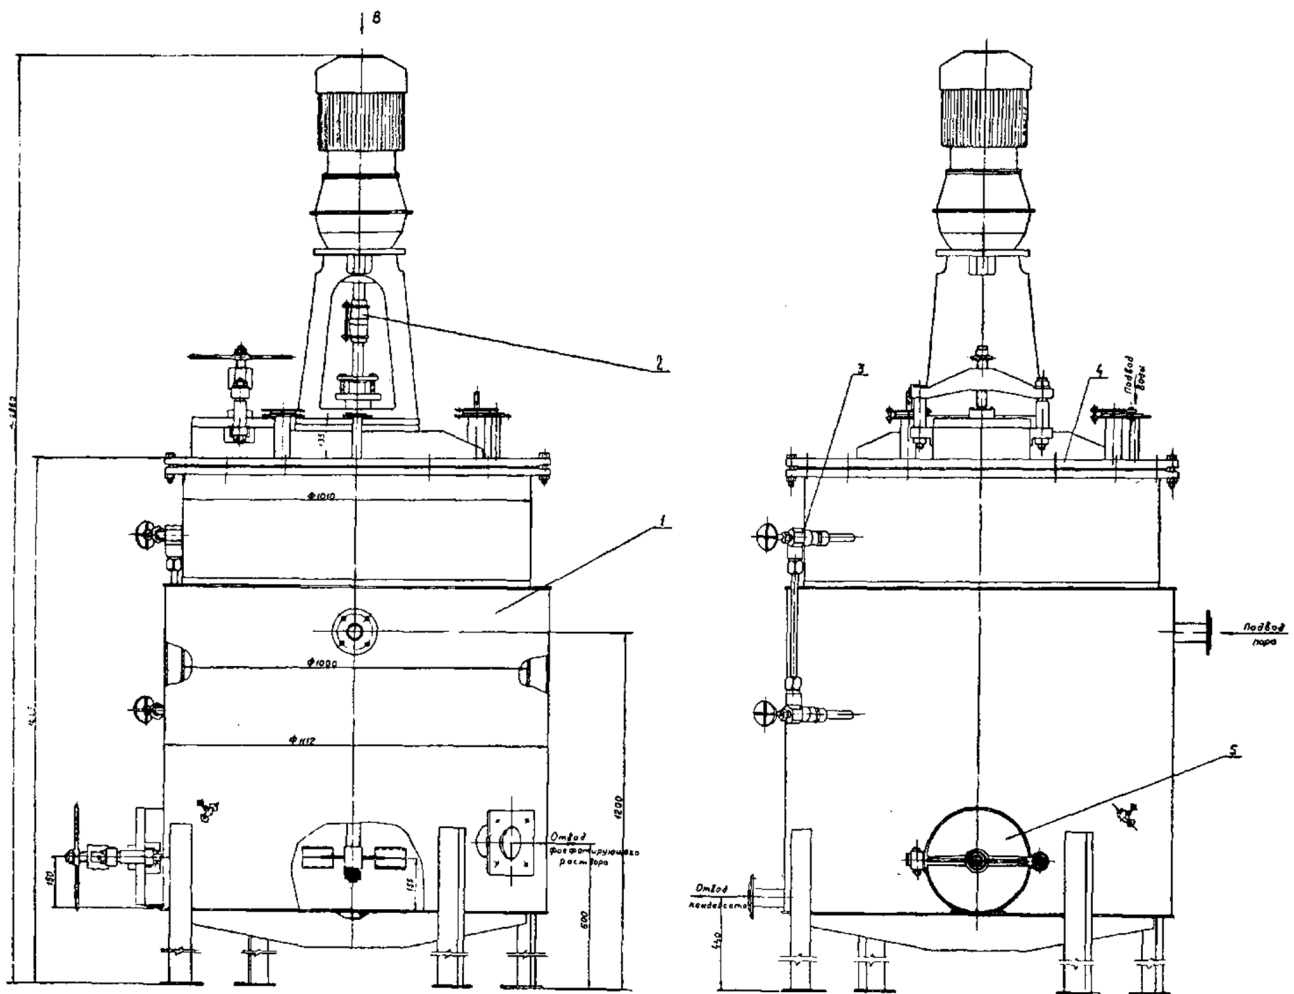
Бак для готування концентрованого фосфатного розчину:
